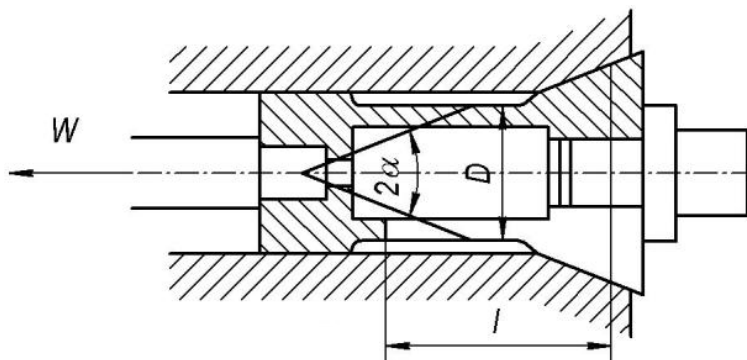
Конструкция цангового патрона с тянущей цангой
